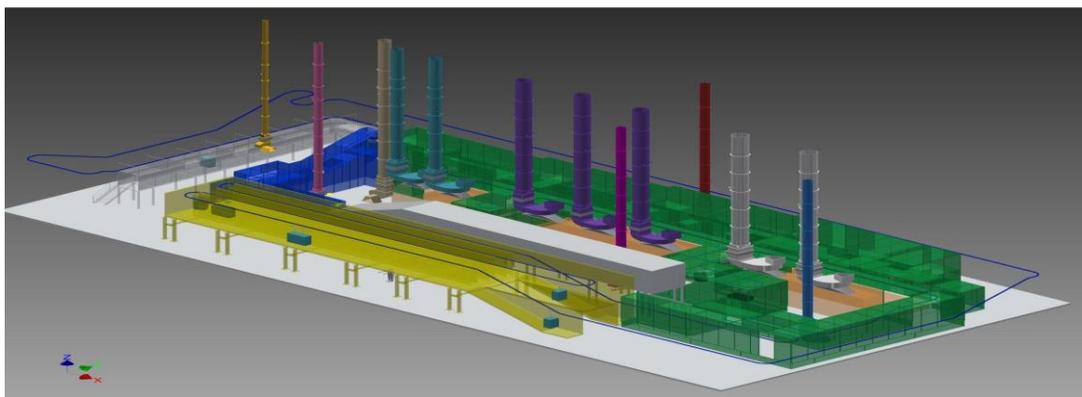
Plano planta pintura Incolmotos Yamaha (Investigadores)
